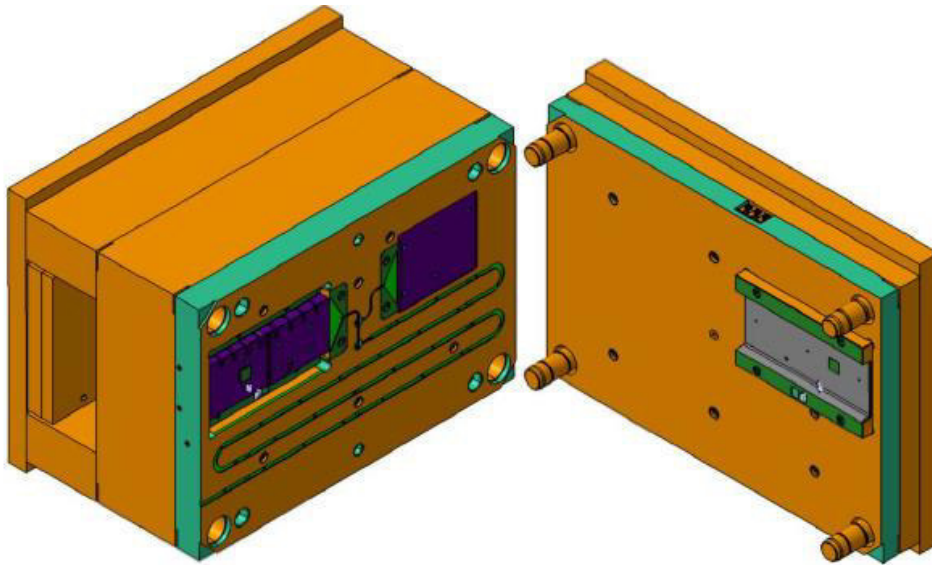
Werkzeug: Platte mit geometrischen Besonderheiten.
